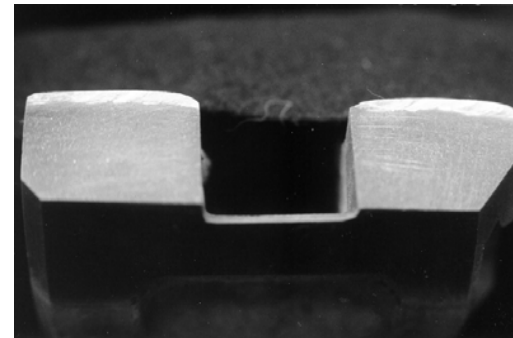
Ремонтная плазменная сварка картера автомобиля.
